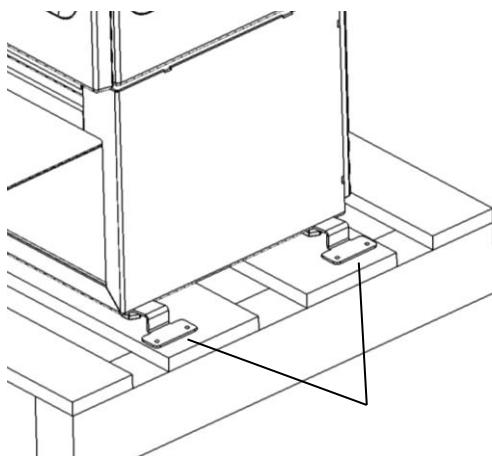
Detalle de las chapas que amarran las patas a la base de madera
